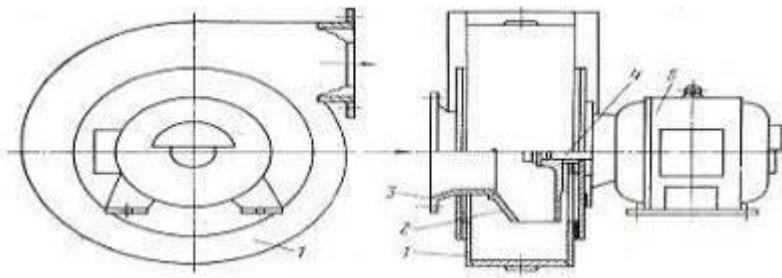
Вентилятор центробежный: 1-корпус; 2 - рабочее колесо; 3-приемный патрубок; 4-вал; 5-электродвигатель.
